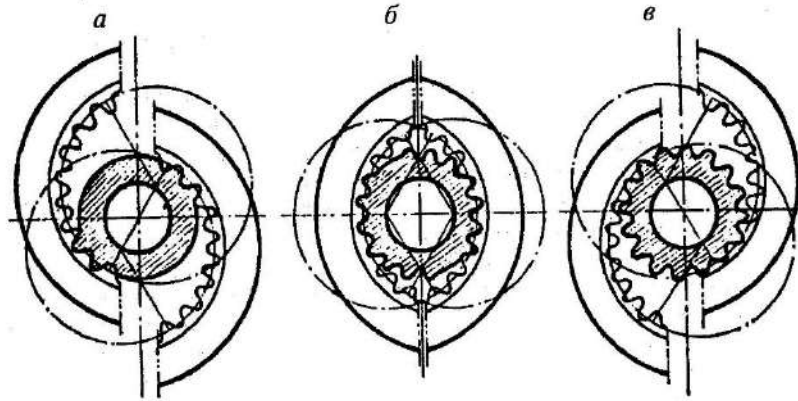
Метод накатки інструментом з внутрішньою формуючою поверхнею:
